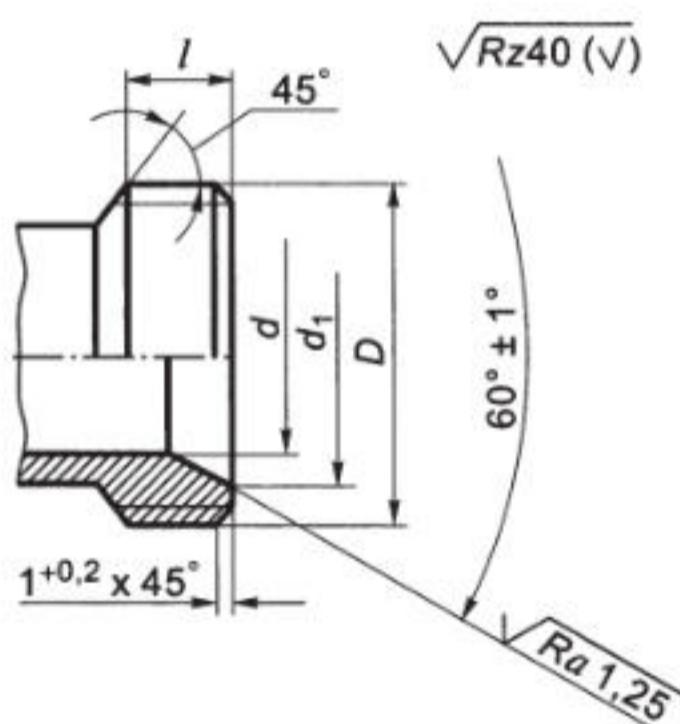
Резьбовая часть арматуры для соединений трубопроводов по внутреннему конусу
